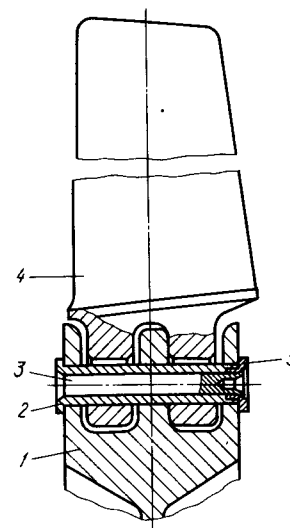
Схема шарнирного крепления лопатки к диску
